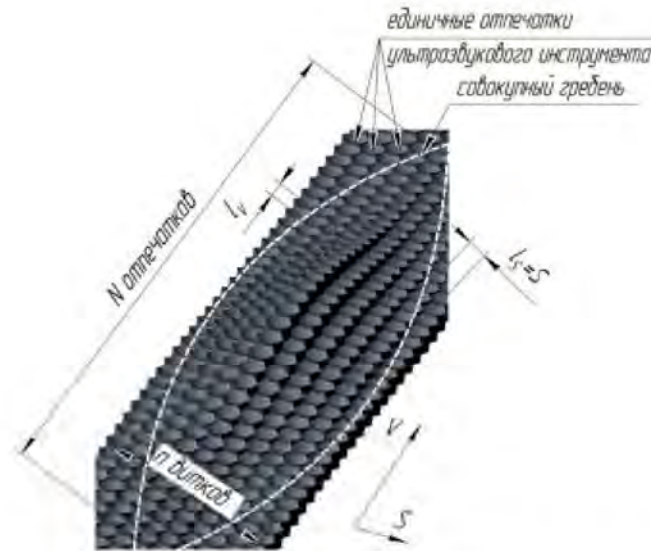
Схематическое изображение совокупного гребня волны при ударах инструмента
